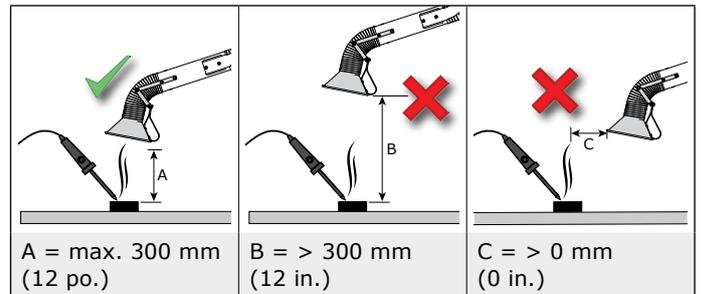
A = Position correcte de la buse (exemple : soudage)
